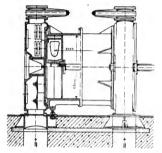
Stumpf - Riedlersches Ventil für schnelllaufende Gebläsemaschinen.
